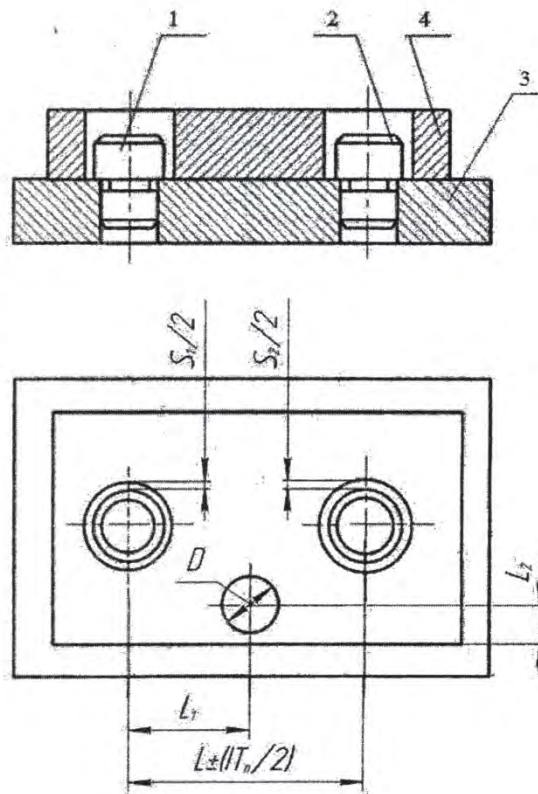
Схема установки заготовки базовыми поверхностями на цилиндрические пальцы
